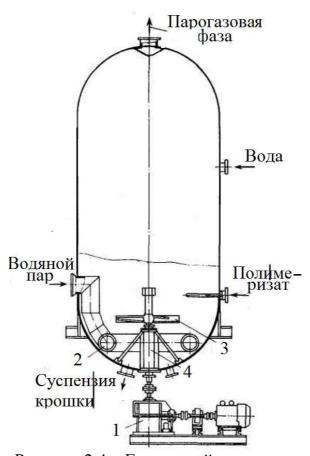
Емкостный дегазатор: 1- привод; 2 – барботер; 3 – мешалка; 4 – подшипниковая опора
